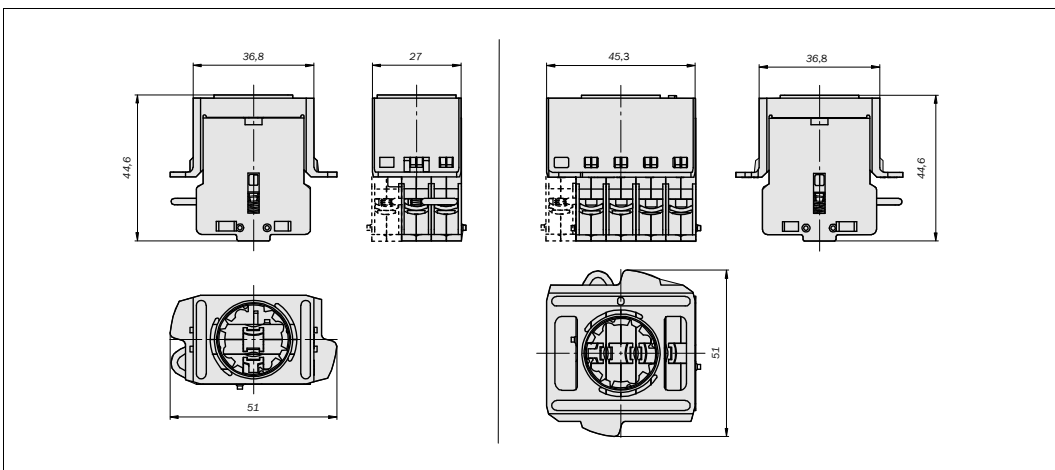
Croquis de dimensiones de los bloques de contacto (mm)
